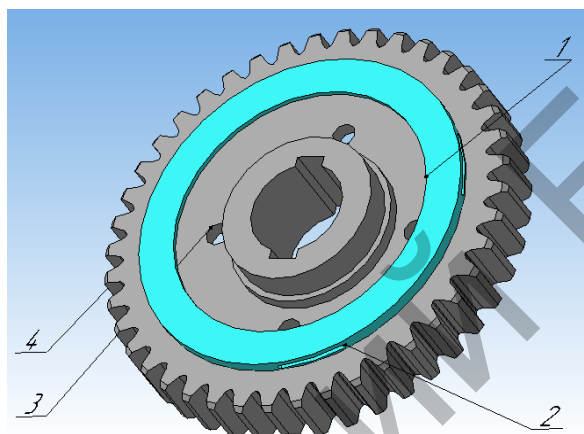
Предлагаемая конструкция шестерни с цилиндрической вставкой
